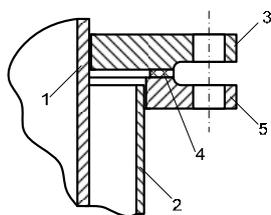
Конструкция съемного крепления рубашки к корпусу сварного аппарата:
